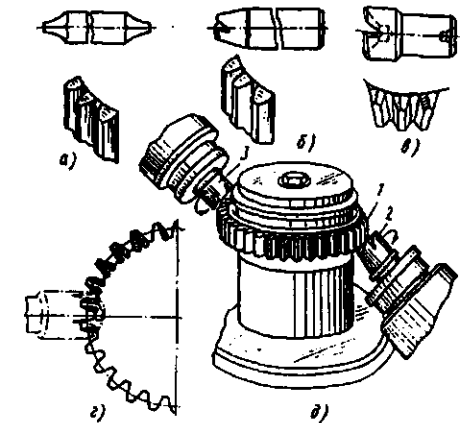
Формы закругления торцов зубьев зубчатых колес
